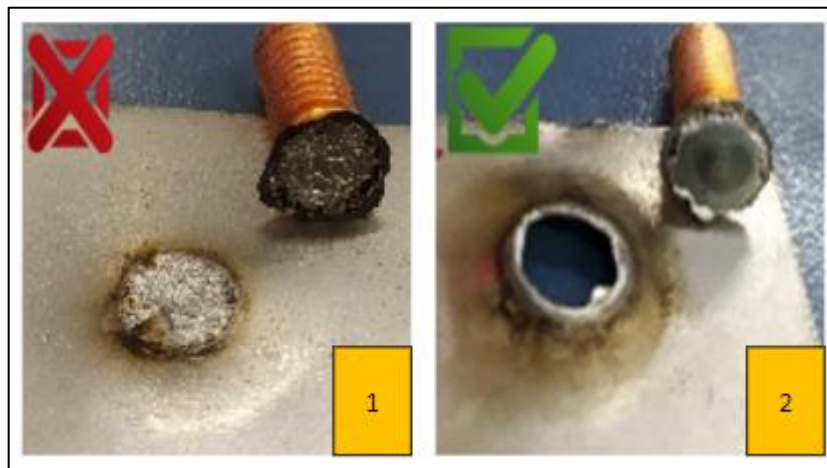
Condição da solda, 1- Solda com defeito (rompido), 2- Solda com boa qualidade.
